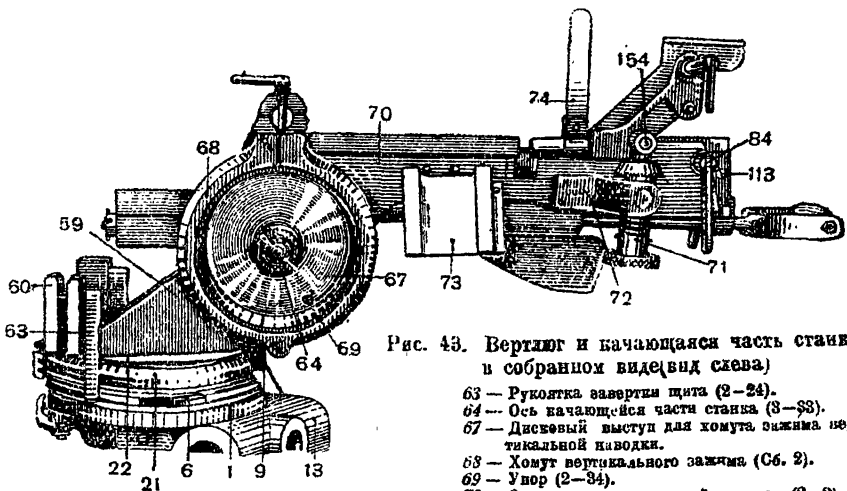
Вертульг и качающаяся часть станка в собранном виде (вид слева)
